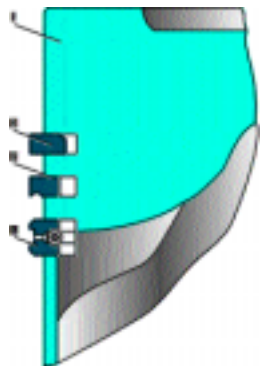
Расположение поршневых колец в канавках поршня двигателя мод. 2106-70: 1 – поршень; 2 – верхнее компрессионное кольцо; 3 – нижнее компрессионное кольцо; 4 – маслоъемное кольцо
